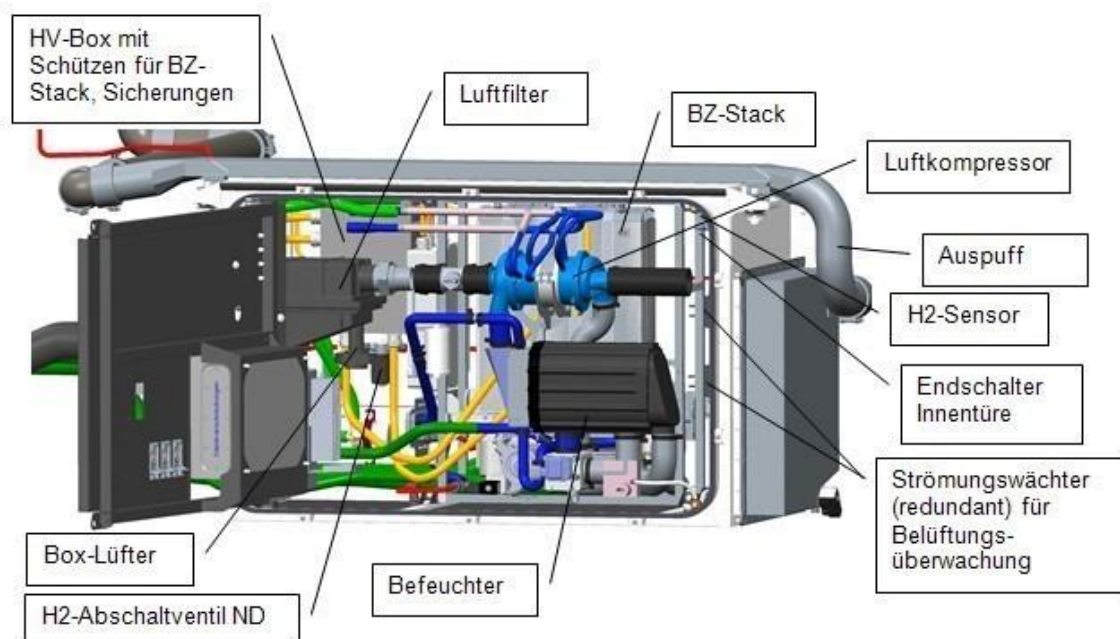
CAD-Seitenansicht der Brennstoffzellenbox mit offener Schwenktüre
